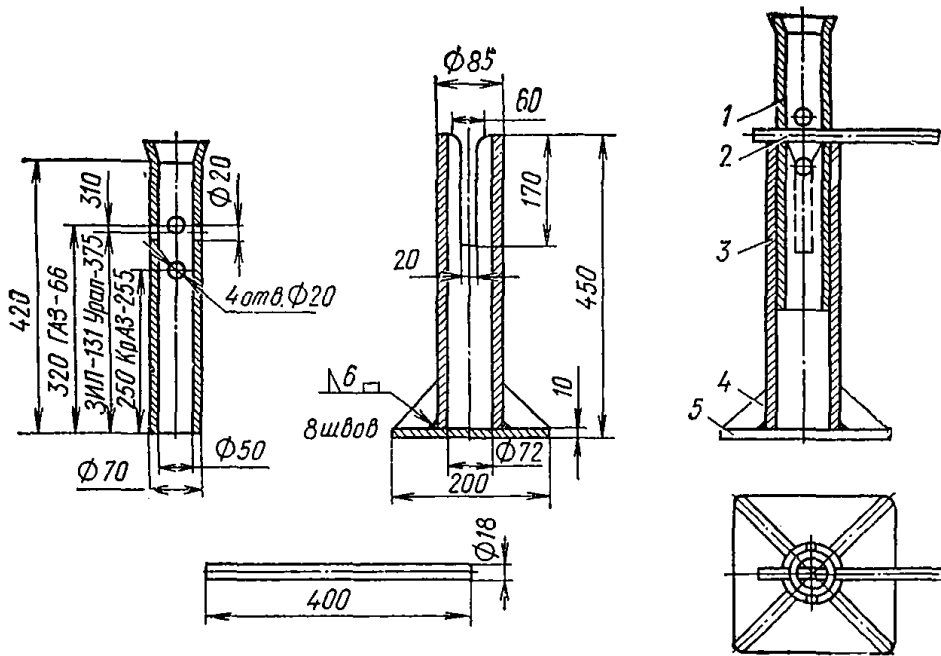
Универсальная саморазгружающаяся подставка для разгрузки колес автомобилей. Размеры, указанные в чертеже, приведены для изготовления подставки для разгрузки колес переднего моста автомобиля.
